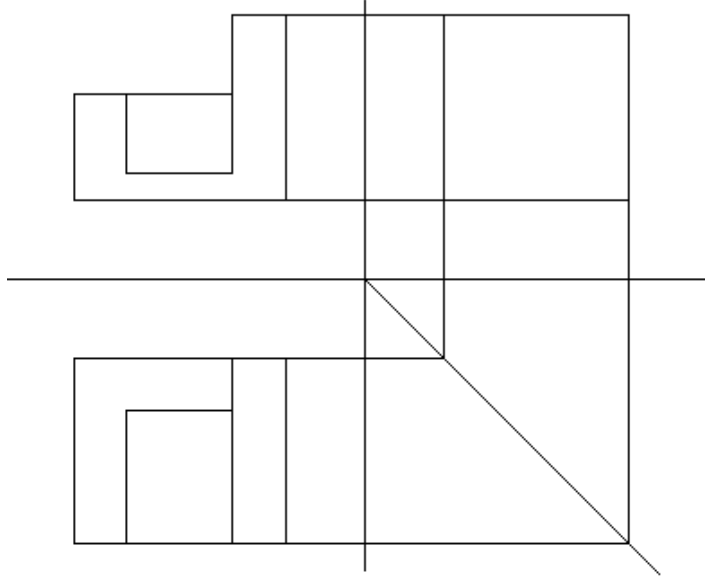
Temel boyutların yatay düzleme taşınması
